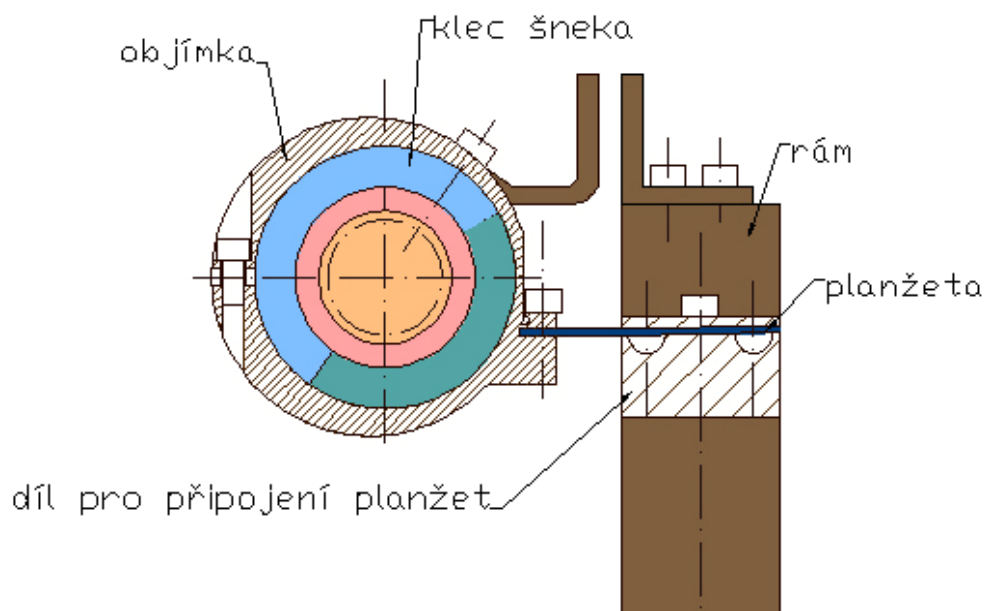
Uložení šneku - pohled z boku, v řezu
